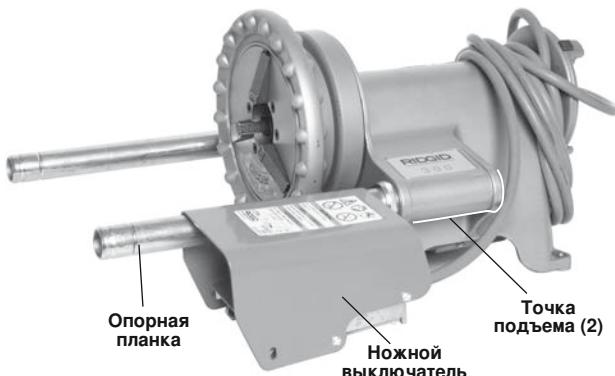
Станок без принадлежностей, подготовленный к транспортировке
